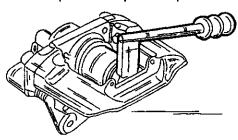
Использование специального инструмента для утапливания поршня в отверстии. Подобное приспособление легко изготовить.
